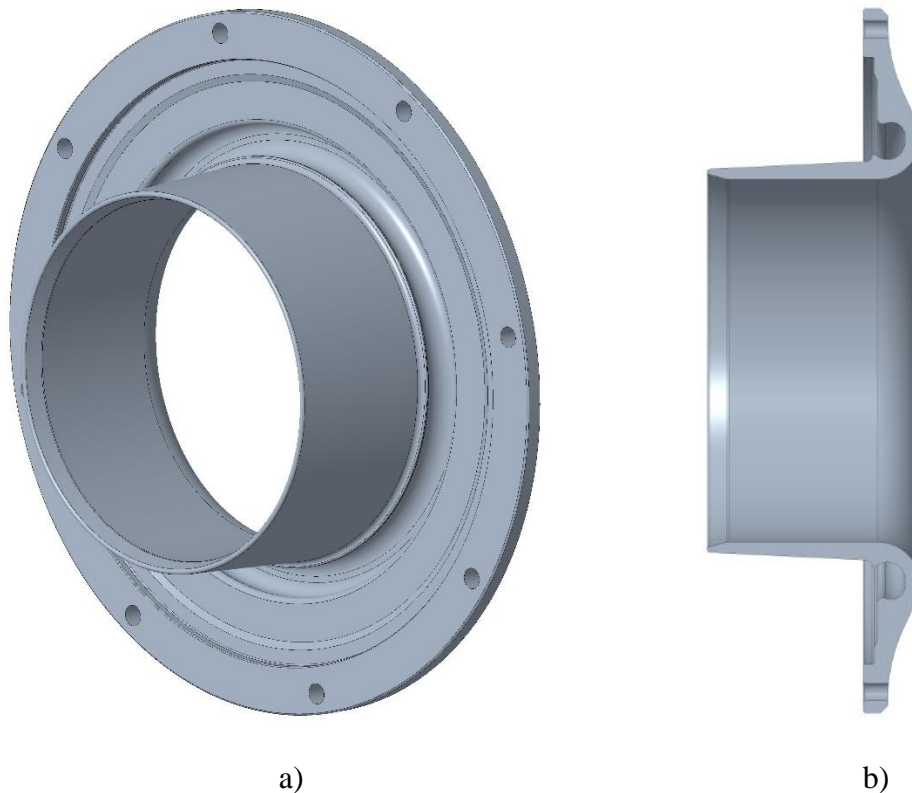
Model příruby: a) obecný pohled, b) zobrazení v řezu
